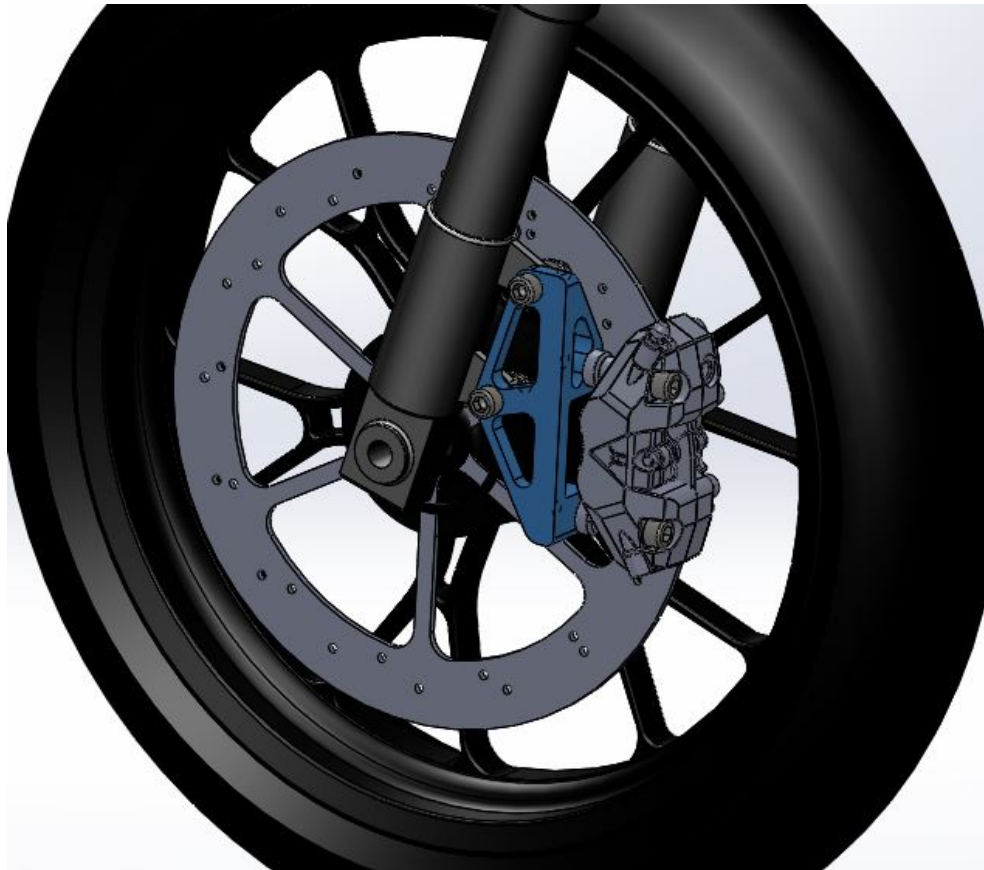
Fabricación. Ensamblaje. Vista cercana.
